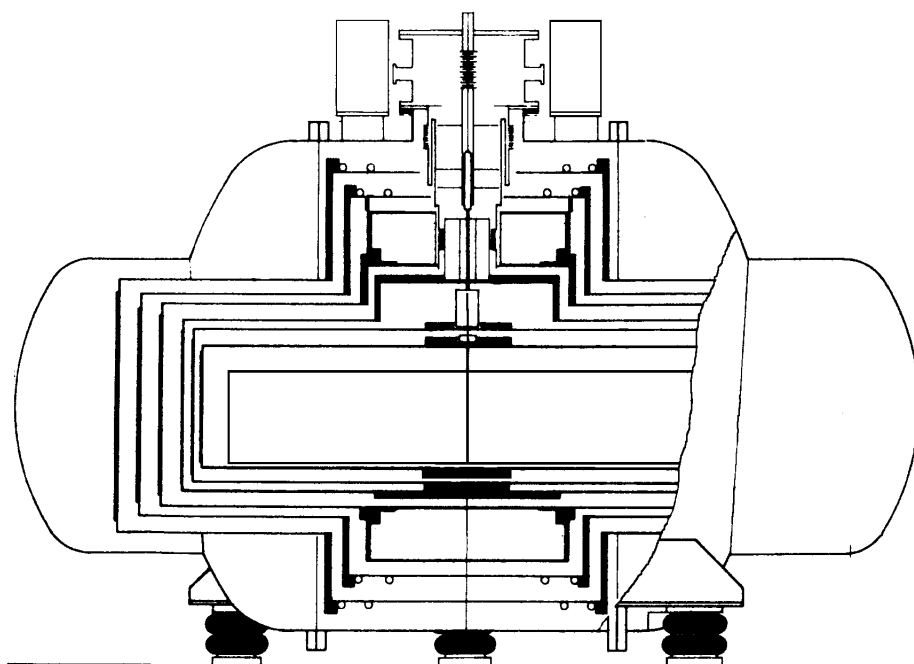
Sezione longitudinale del criostato AURIGA
